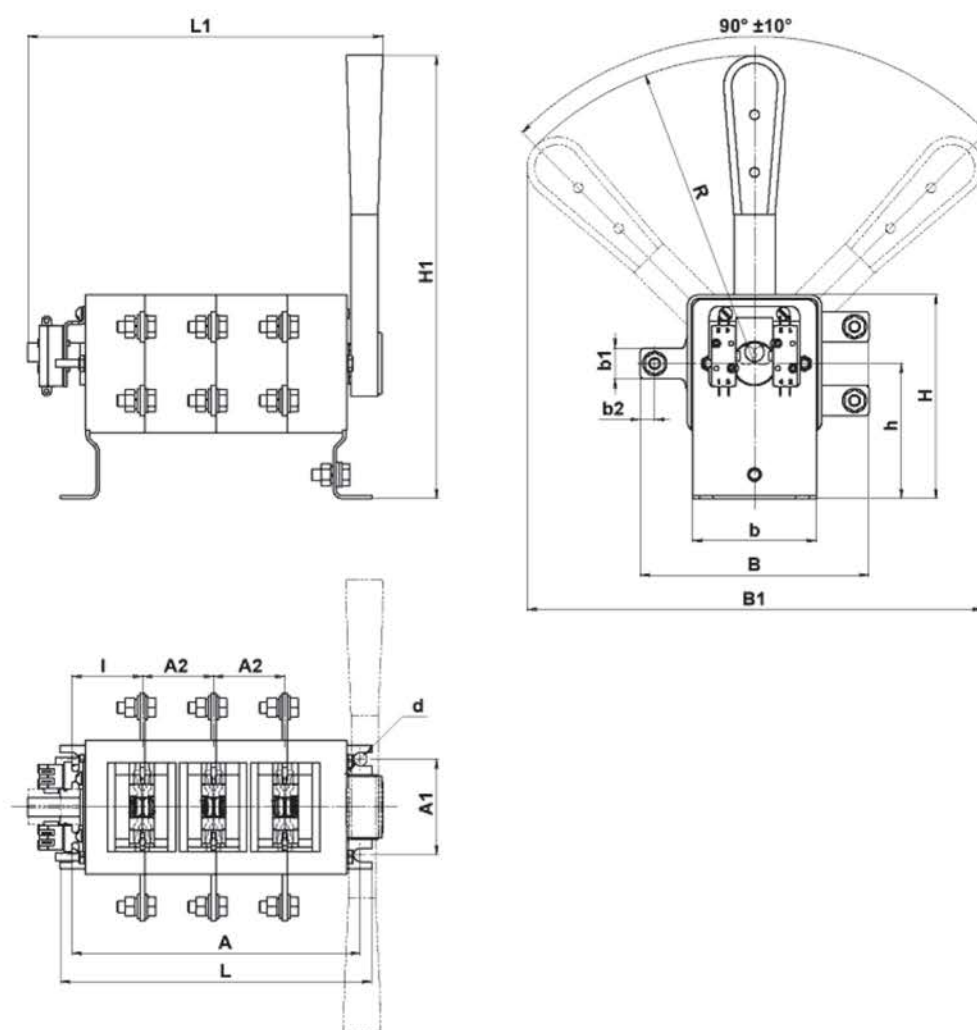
Выключатель-разъединитель трехполюсный на два направления с передней смещенной рукояткой.
